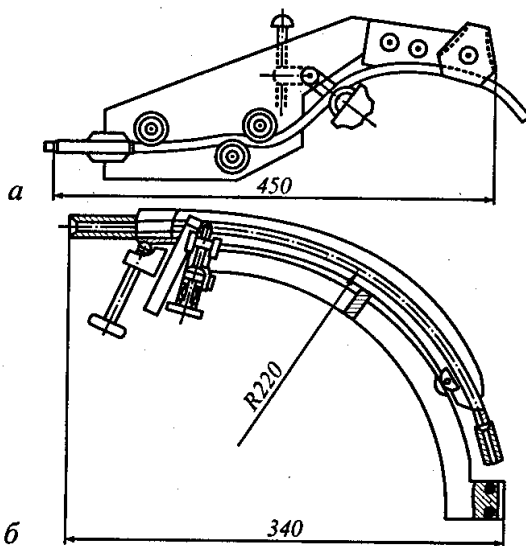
Схемы мундштуков для электрошлаковой сварки проволочными электродами:
